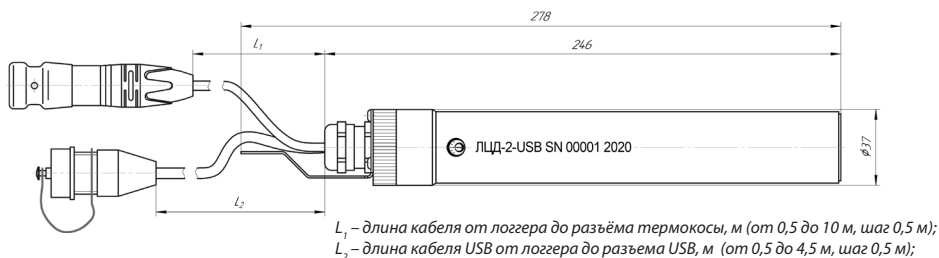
Габаритный чертеж логгера цифровых датчиков ЛЦД-2-USB
